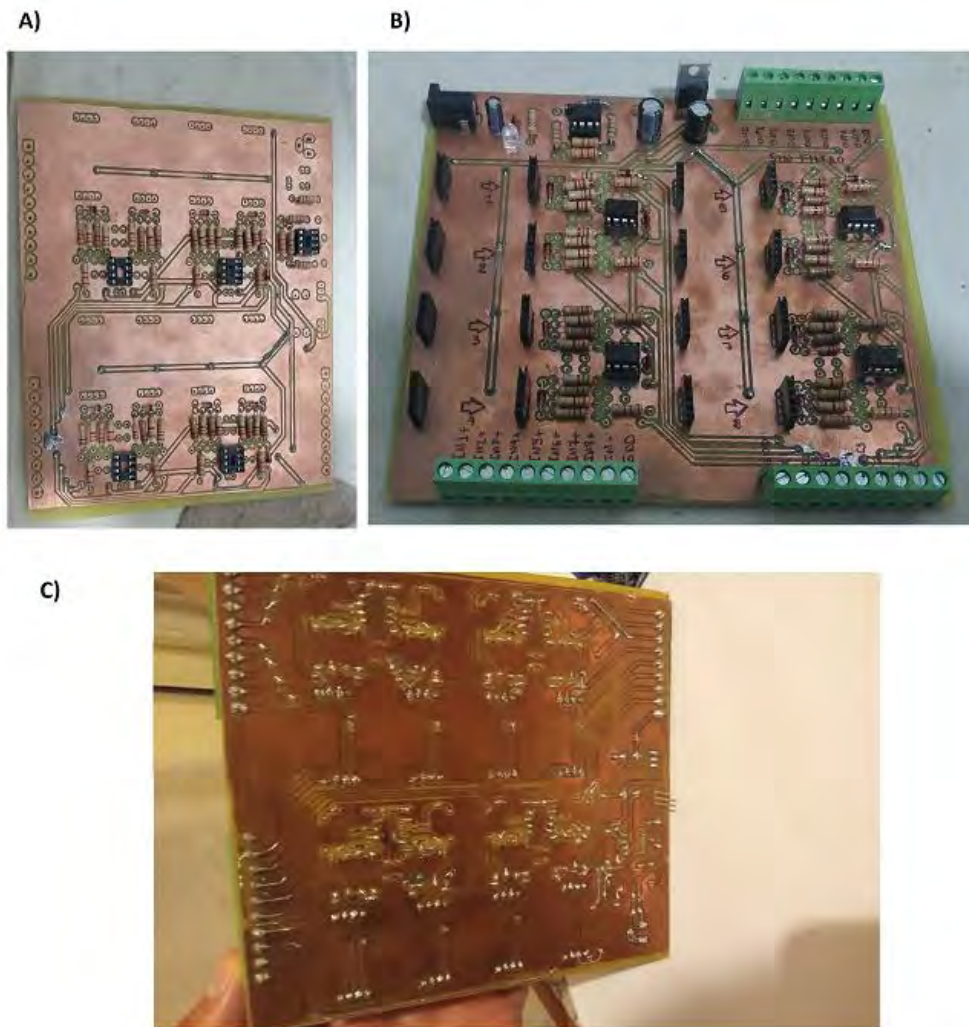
Soldadura de componentes. A) Imperfecto a causa de levantamiento de pista en la placa. B) Etapa de amplificación terminada, procesos cerca de finalización. C) Parte inferior de la placa
